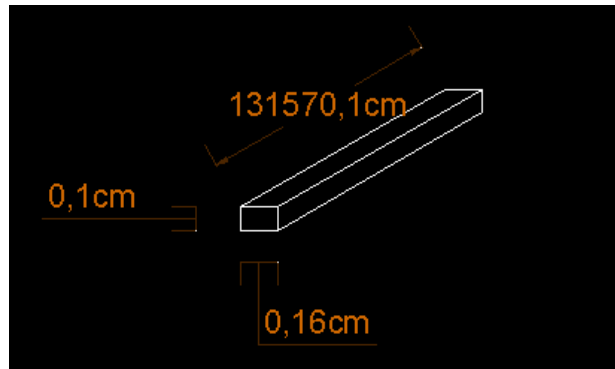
Dimensiones geométricas del conductor de alta tensión.
